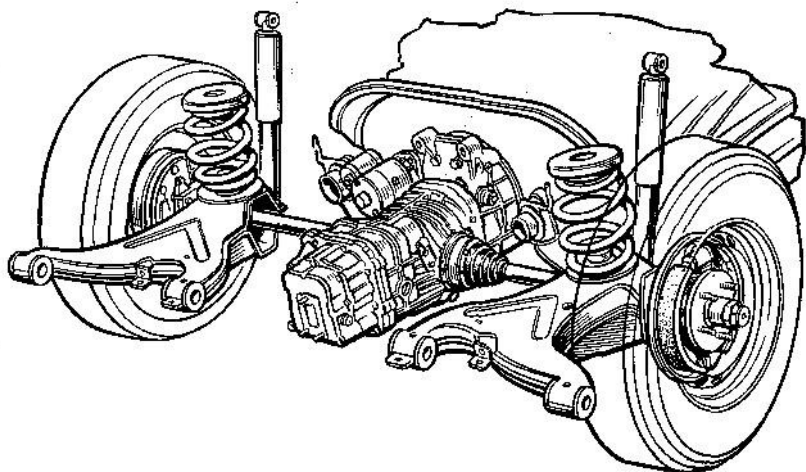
Задняя подвеска автомобиля «Фольксваген-транспортёр» с коробчатыми косыми рычагами, непосредственно прикрепляемыми к кузову. Хорошо виден блок трансмиссии с фланцевым креплением к двигателю заднего расположения
